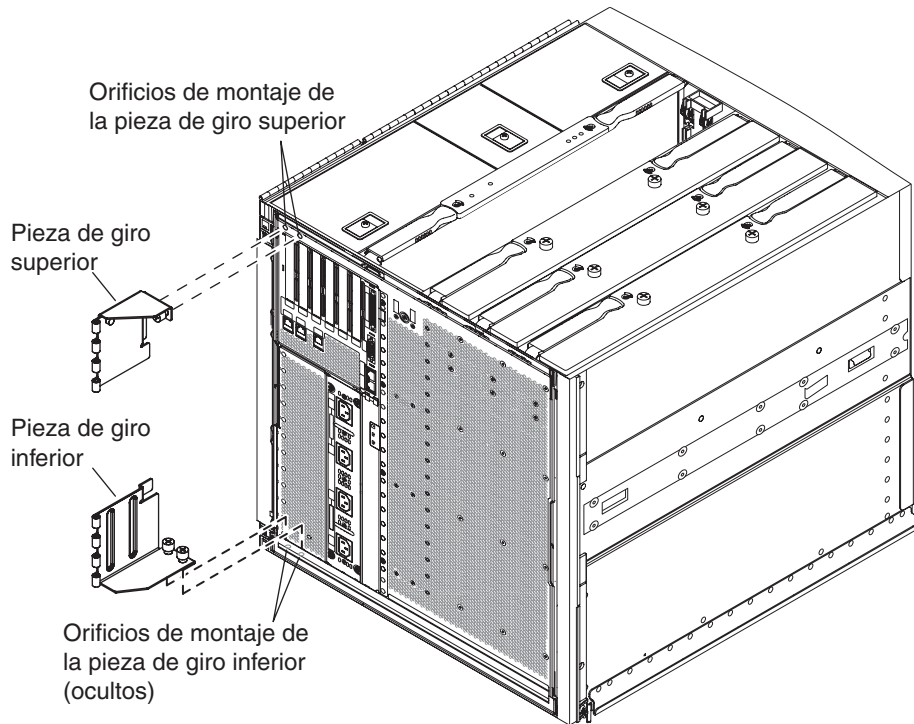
Orificios de montaje de las pieza de giro superior e inferior
